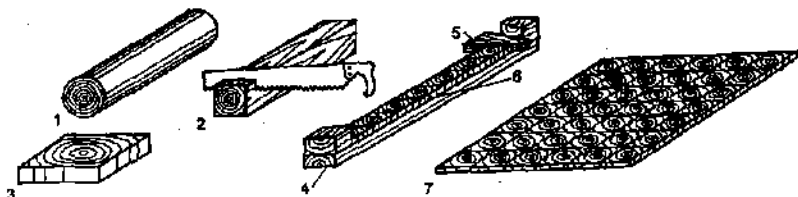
Последовательность изготовления клееной торцовой плиты: 1 — заготовка; 2 — брусок; 3 — пластинка; 4 — приспособление; 5 — клип; 6 — полоска из пластинок; 7 — плита
